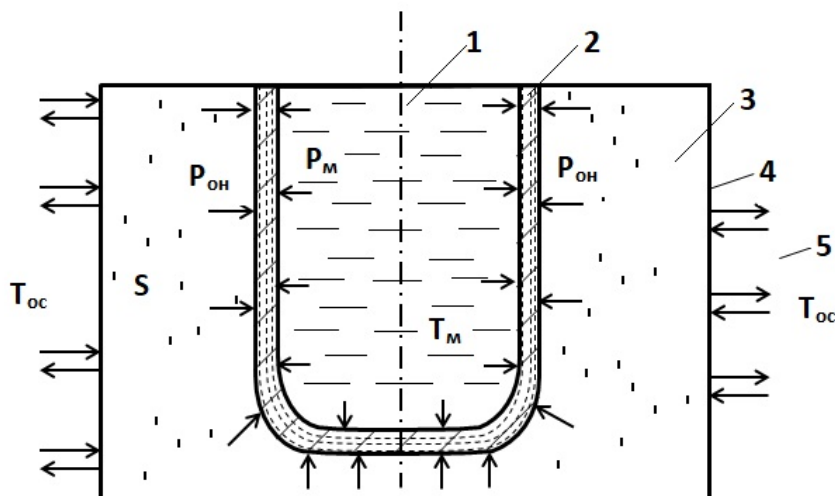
Схема заформованной в опорный наполнитель оболочковой формы и залитой жидким металлом: 1 – жидкий металл; 2 – оболочковая форма; 3 – опорный наполнитель; 4 – опока (кожух); 5 – окружающая среда. T_{oc} – температура окружающей среды; T_m – температура жидкого металла; P_m – давление жидкого металла на оболочковую форму; $P_{он}$ – давление опорного наполнителя на оболочковую форму
